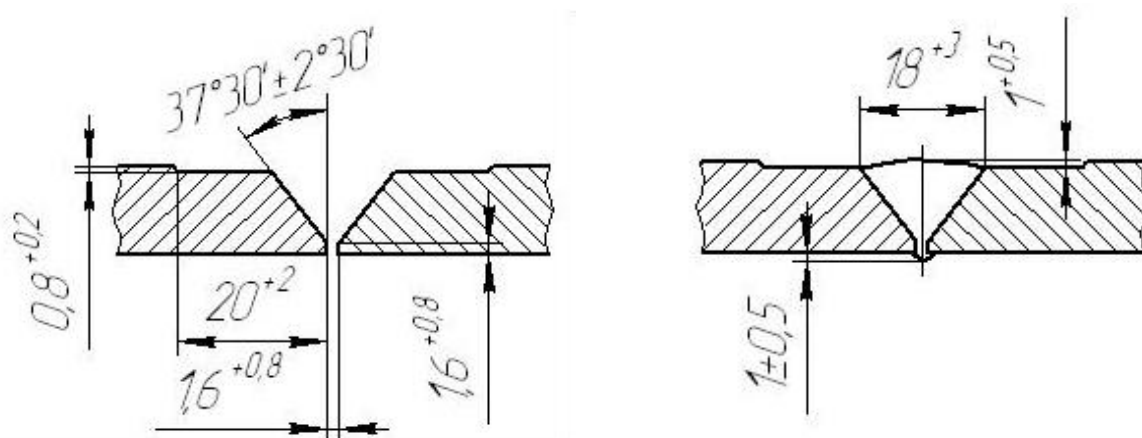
Подготовка кромок и форма сварного шва при выполнении стыкового кольцевого шва № 2 и шва № 3
